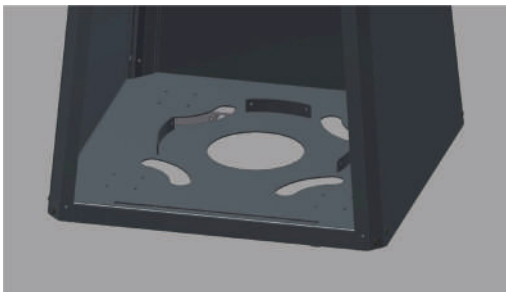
Схематичний малюнок нижніх опор газового балона, до яких кріпиться балон після монтажу.
